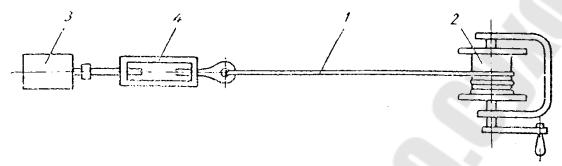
Схема монтажа выключающего устройства: 1 — трос (проволока); 2 — барабан; 3 — выключатель; 4 — стяжное устройство
